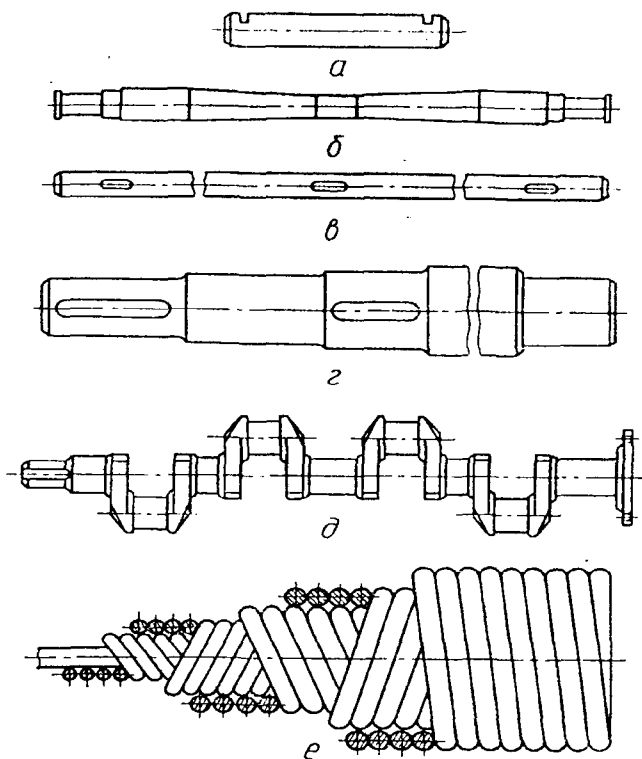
Оси и валы: а - невращающаяся ось; б - вращающаяся ось; в - гладкий прямой вал; г - ступенчатый прямой вал; д - коленчатый вал; е - гибкий вал
